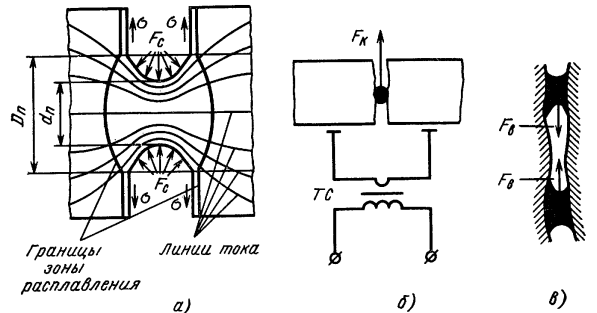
Силы, действующие на перемычки при сварке оплавлением
